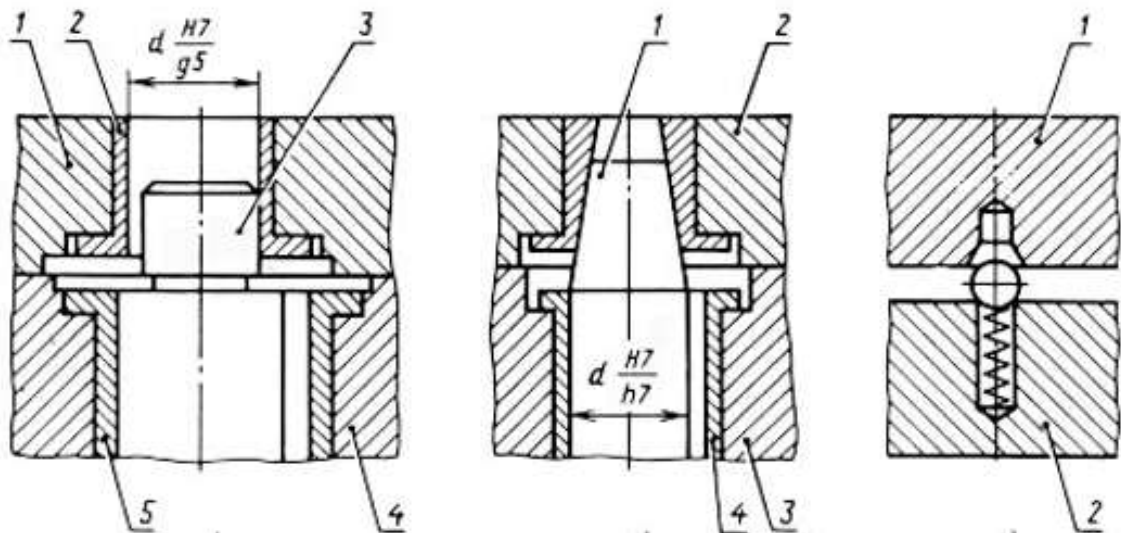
Фіксатори ділільних пристроїв: а - з циліндричним пальцем (1 - поворотна частина пристрою; 2, 5 - втулки; 3 - циліндричний фіксатор; 4 - корпус пристрою); б - з конічним пальцем (1 - конічний палець; 2 - поворотна частина пристрою; 3 - корпус пристрою; 4 - втулка); в - кульковий (1 - поворотна частина пристрою; 2 - корпус пристрою)
